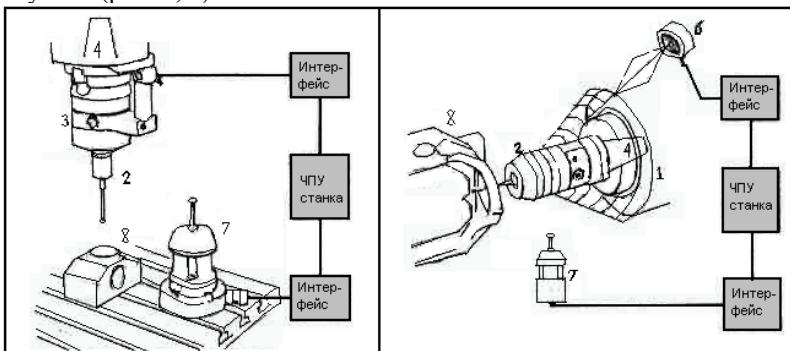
Применение контактных датчиков на обрабатывающих центрах и фрезерных станках: 1 - шпиндель станка; 2 - контактный датчик; 3 - адаптер; 4 - установочный конус; 5 - модули системы индуктивной передачи данных; 6 - оптический приемник; 7 - датчик наладки инструмента; 8 - обрабатываемая деталь.
